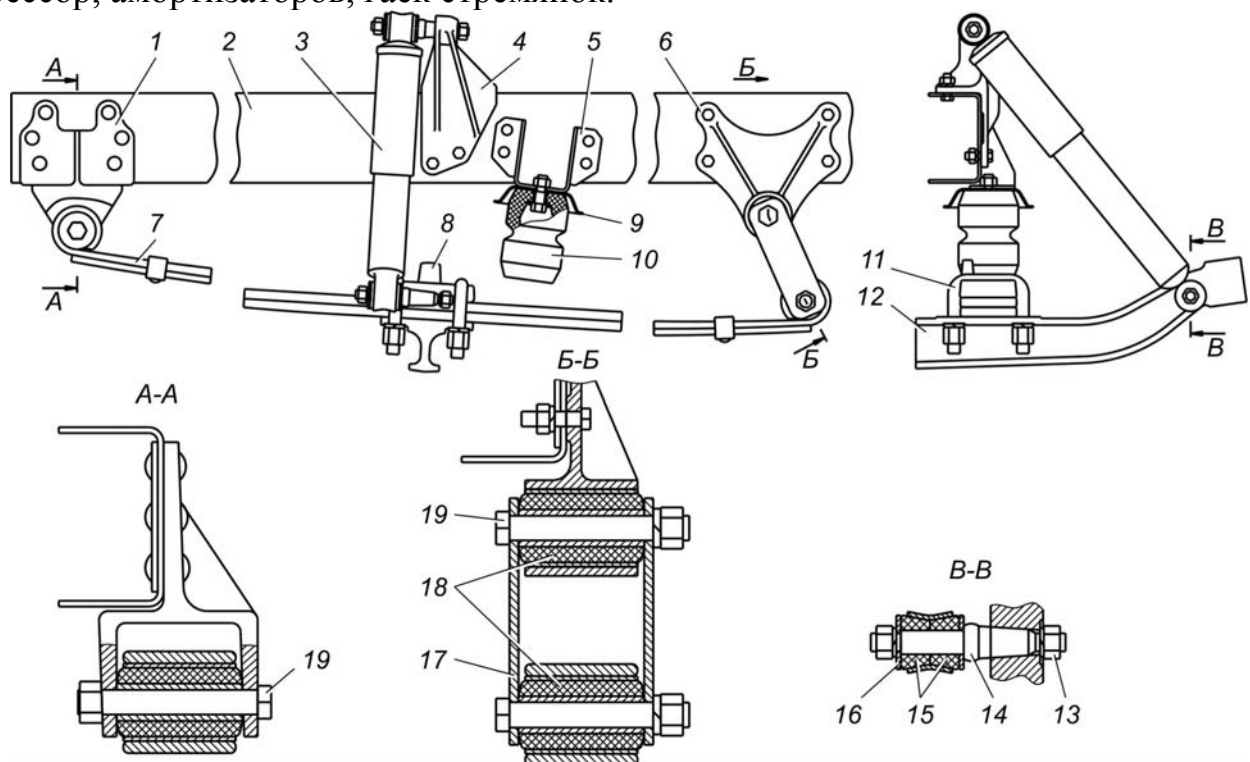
Передняя подвеска автомобилей типа 4х2: 1, 4, 5 и 6 – кронштейны; 2 – лонжерон рамы; 3 – амортизатор; 7 – рессора; 8 – накладка; 9 – чашка буфера; 10 – буфер; 11 – стремянка; 12 – балка; 13 – гайка; 14 – палец; 15 – резиновые втулки; 16 – шайба; 17 – серьга; 18 – резинометаллические шарниры; 19 – болт
